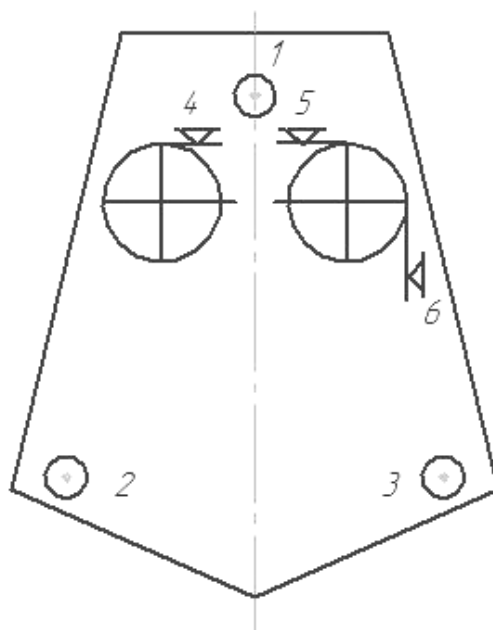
Схема базування і закріплення деталі на операції 030.
